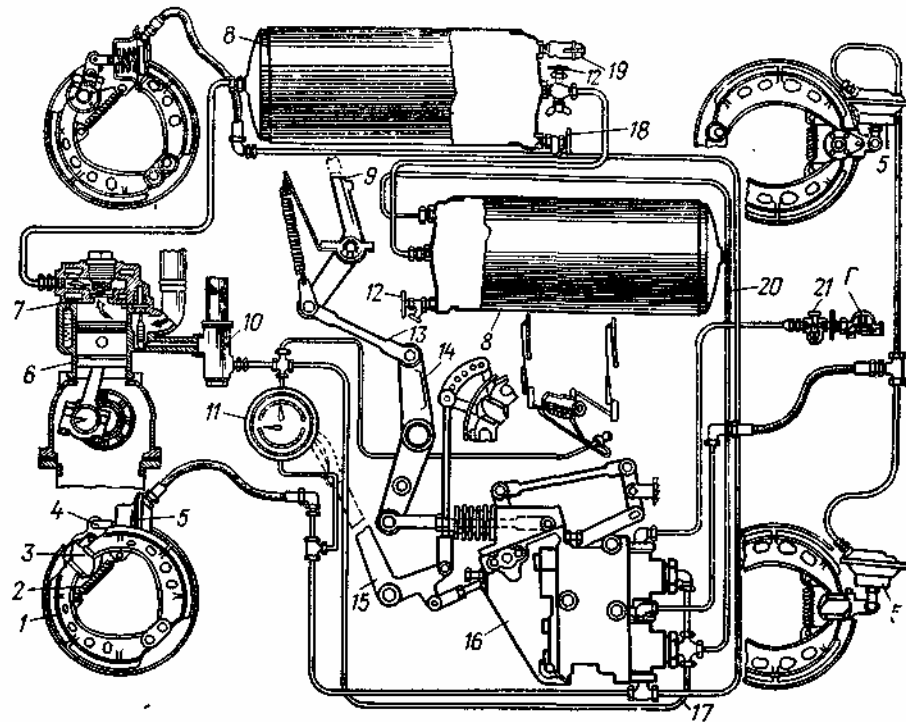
Схема пневматического привода тормозов автомобиля ЗИЛ-130
